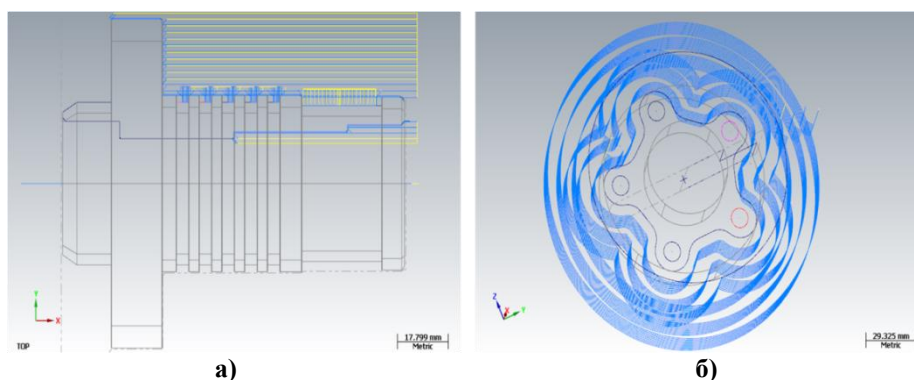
Траектории движения режущих инструментов при токарной (а) и фрезерной (б) операциях. Линии синего цвета – перемещение режущего инструмента на рабочей подаче, желтого цвета – перемещение режущего инструмента на ускоренной подаче.
